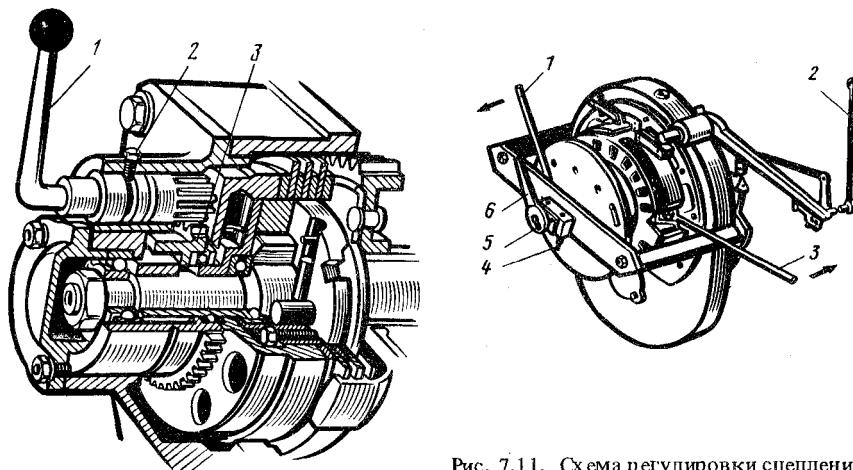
Схема регулировки муфты сцепления пускового двигателя ПД-10УД
